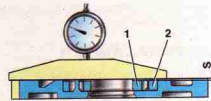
Замер осевых зазоров шестерен масляного насоса: 1 – ведущая шестерня; 2 – ведомая шестерня; S – осевой зазор
